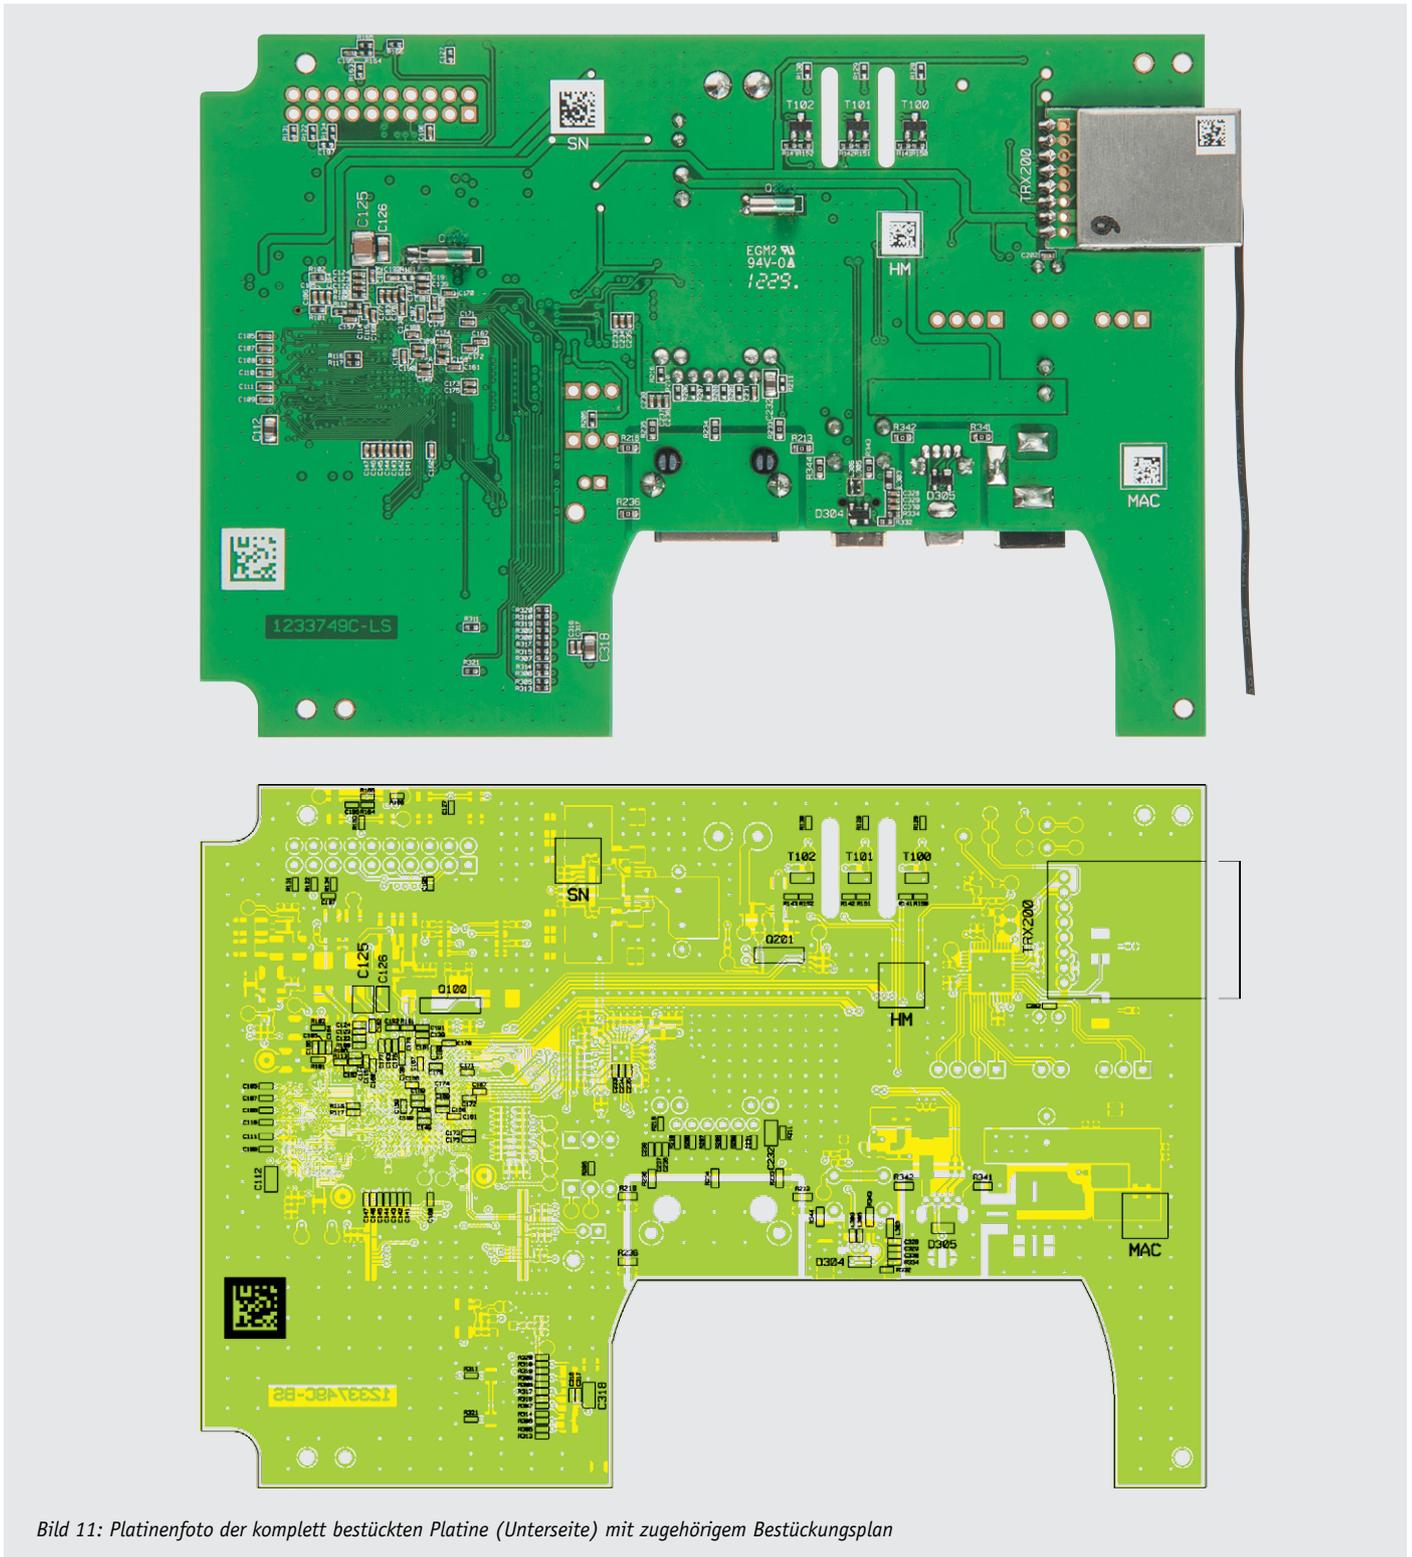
Platinfoto der komplett bestückten Platine (Unterseite) mit zugehörigem Bestückungsplan
